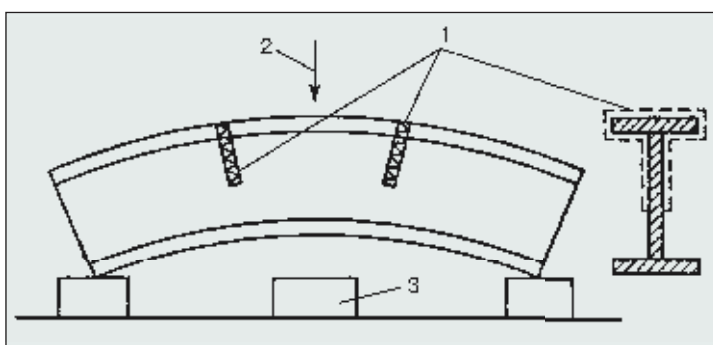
Термо-механическая правка изгиба оси элемента: 1 — полосы нагрева; 2 — груз, устанавливаемый до начала нагрева; 3 — страхующая подкладка
